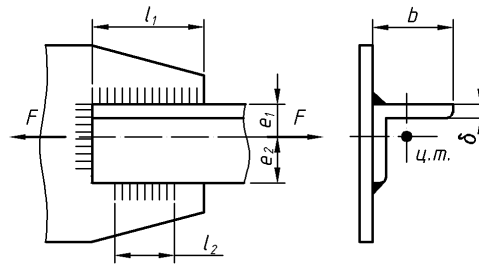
Сварное соединение полосы с косынкой
